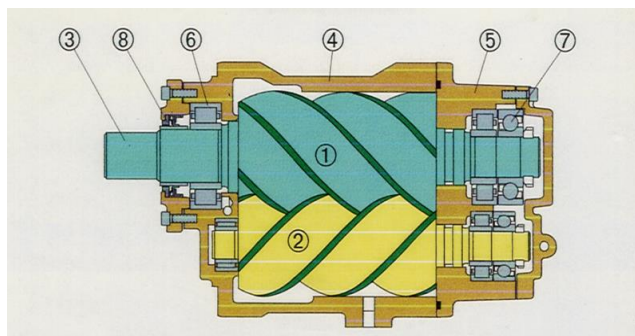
Устройство винтового компрессорного модуля OS70
